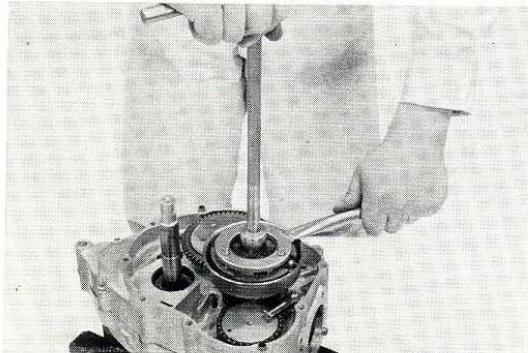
DEMONTAGE DE L'EMBRAYAGE.
